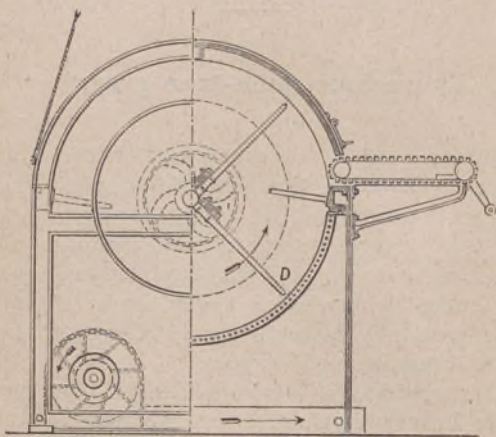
Disegno schematico di battitore. - *D* caviglie disposte ad elica sul tamburo.
